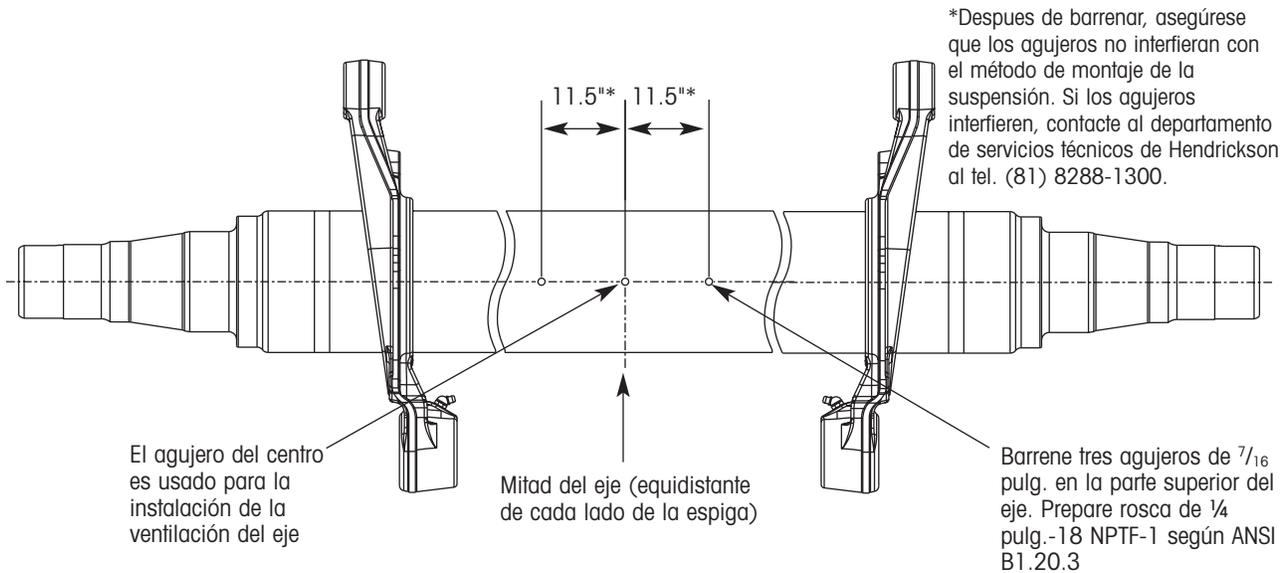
Detalles de barrenado del Eje Hendrickson para Remolques
